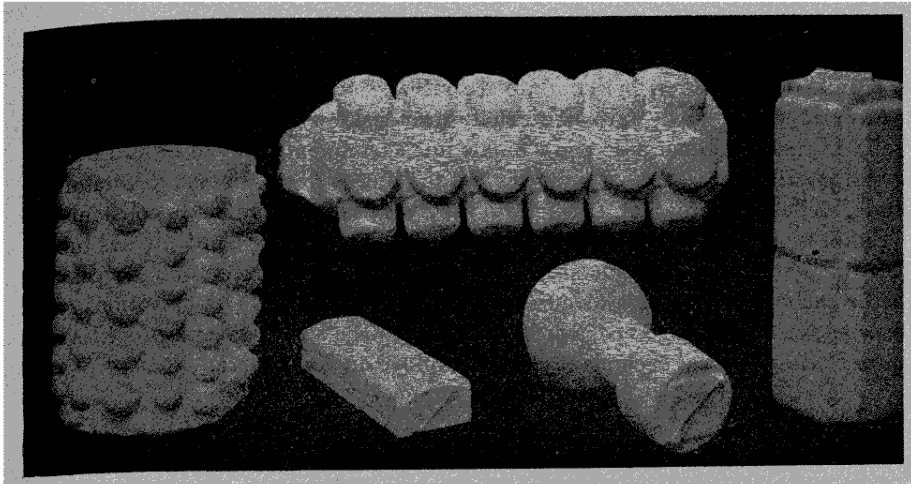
Vue de quelques pièces brutes de silice fondue après le moulage et avant le découpage.
